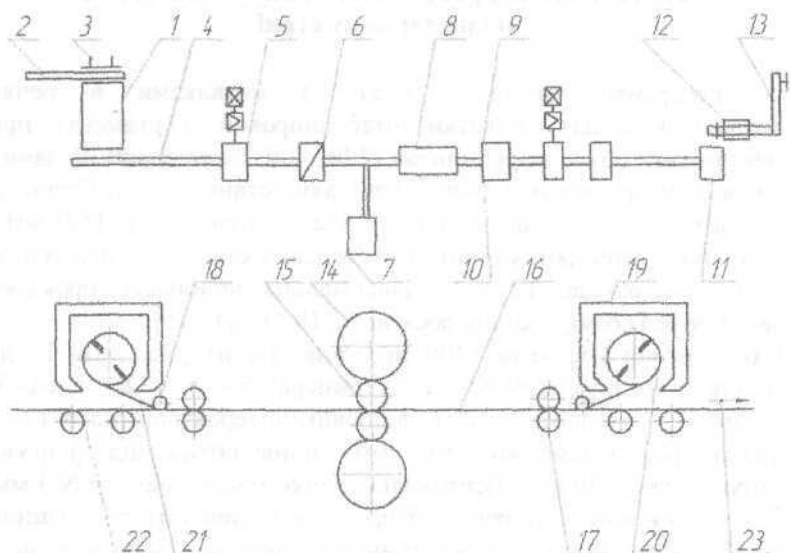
Схема розташування устаткування стана Стекла: 1 - нагрівальні печі; 2 - рольганг; 3 - штовхач; 4 - рольганг; 5 - універсальна кліть; 6 - ножиці; 7 - конвейер для прибирання обриси; 8 - нагрівальна піч з роликової подиною завдовжки 50 м; 9 - печі з моталками; 10 - реверсивна кліть кварто; 11 - моталка готової штаби; 12 - пристрій для прибирання рулонів; 13 - транспортер для рулонів; 14 - опорні валки; 15 - робочі валки; 16 - штаба; 17 - ролик, що направляють; 18 - ролик, що направляє; 19 - піч; 20 - моталка; 21 - проводка; 22 - рольганг; 23 - до моталок 11.
